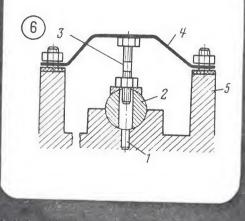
/ Временное крепление валика клапанного механизма: 1 — отверстие с сорванной резьбой; 2 — валик; 3 — шпильна; 4 — крышна; 5 — головка.
